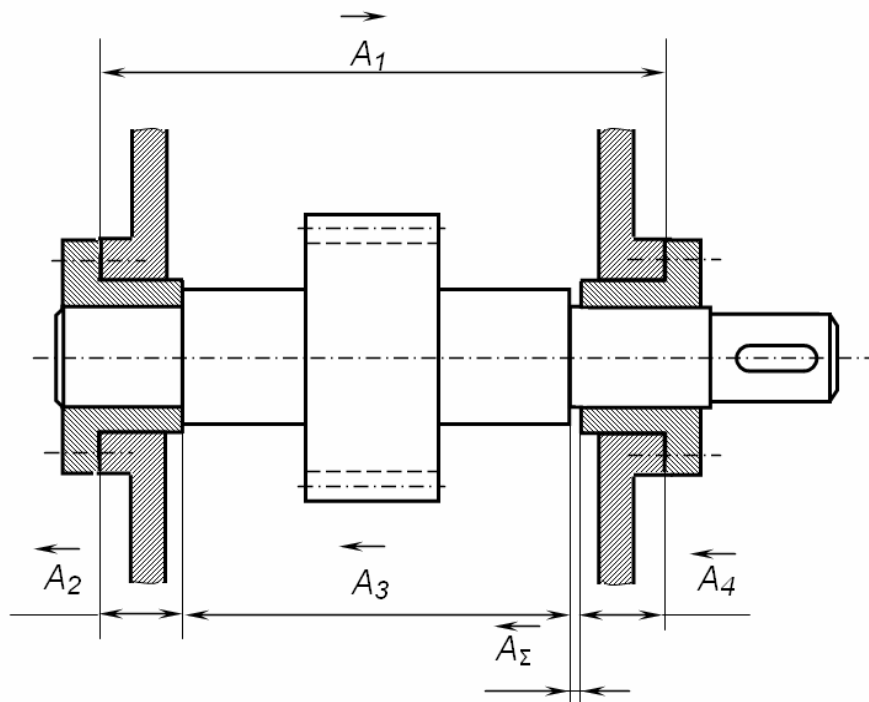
Розрахункова схема вузла редуктора з розмірним ланцюгом
